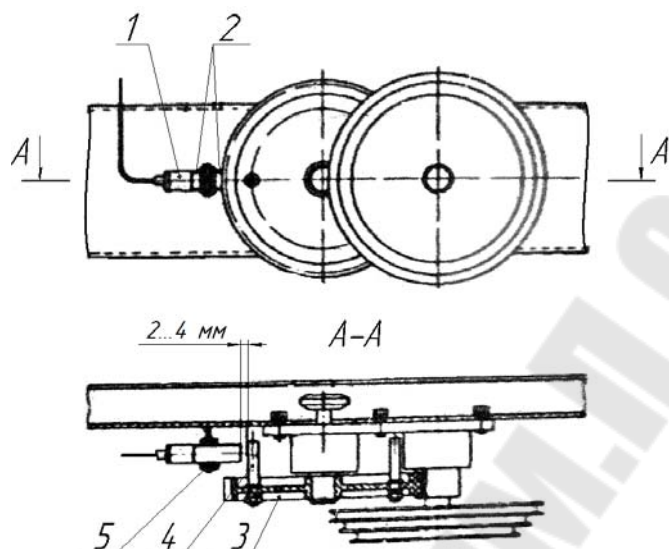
Схема регулировки датчика на обматывающем аппарате: 1 – датчик; 2 – гайки; 3 – кронштейн; 4 – шунт; 5 – шестерня
